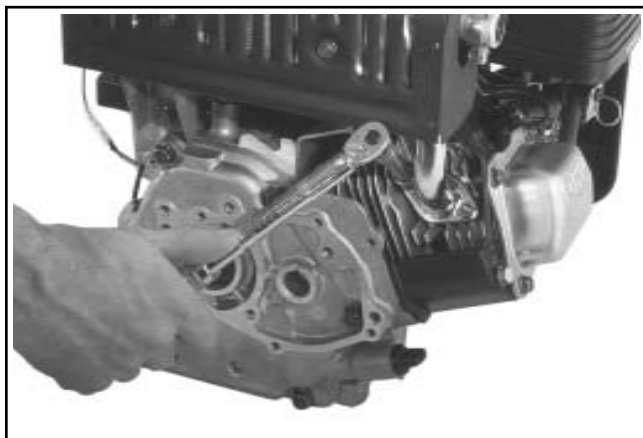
Serraggio delle viti di montaggio del silenziatore.
